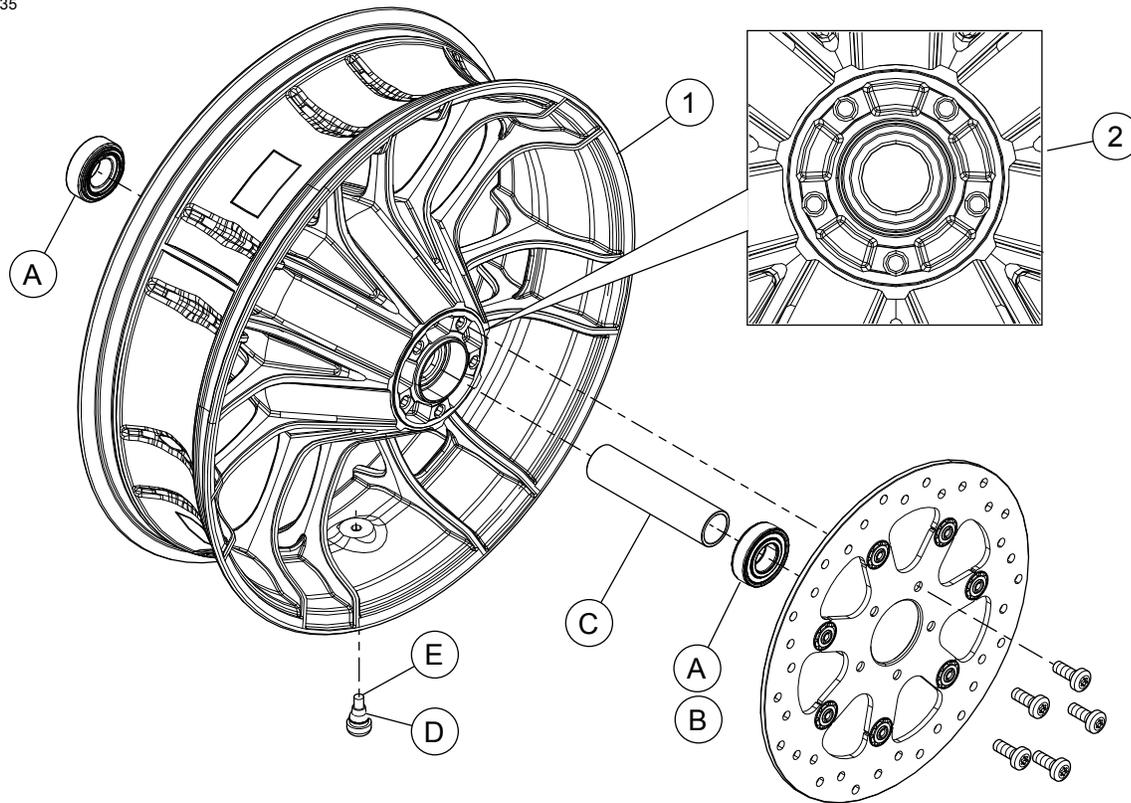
Ersatzteile: Knockout Rear Wheel
